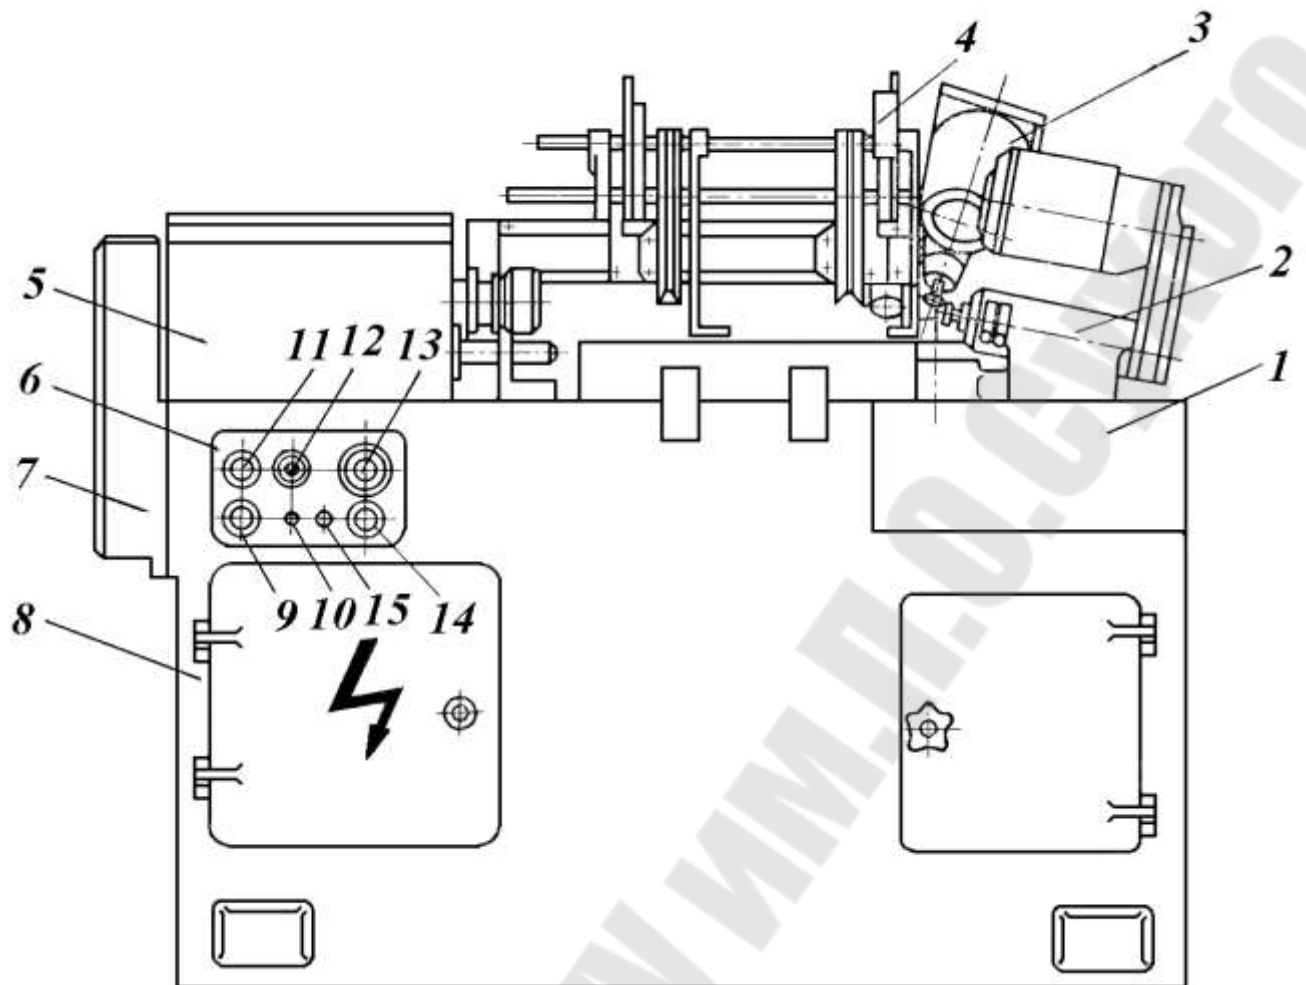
Эскиз специального сверлофрезерного автомата модели СИ-031:
